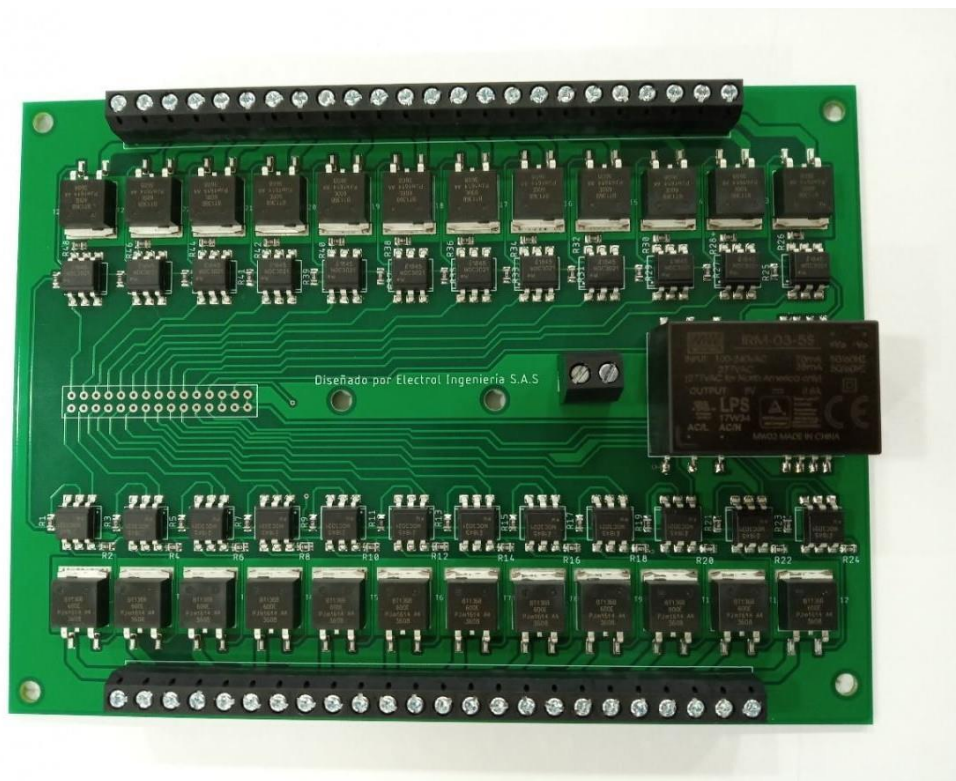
Componentes SMD soldados en tarjeta PCB AC. Tobón. (2019)
